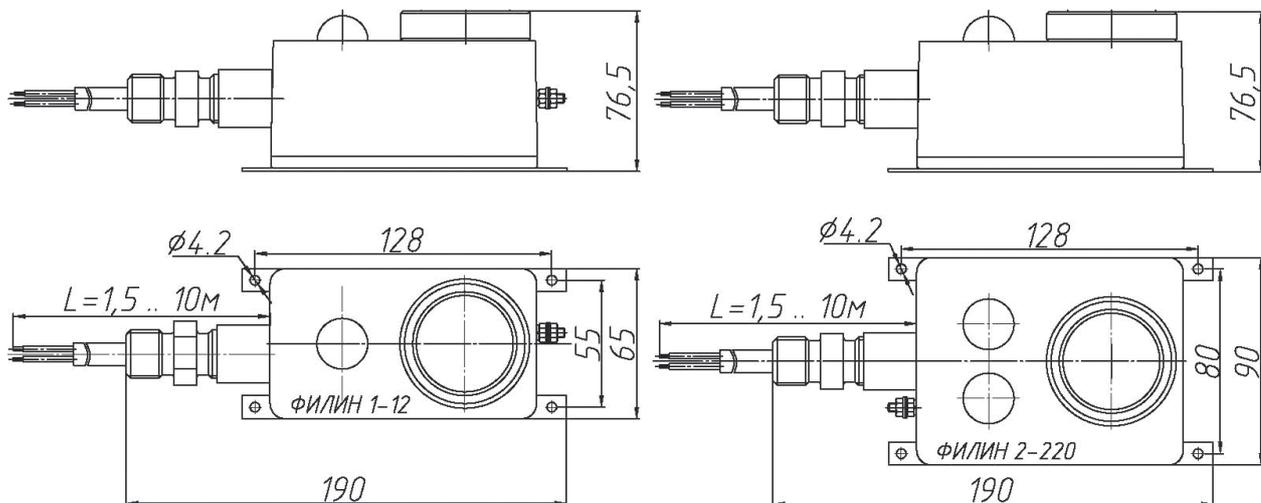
Габаритные и присоединительные размеры светозвукового Оповещателя Филлин-1
